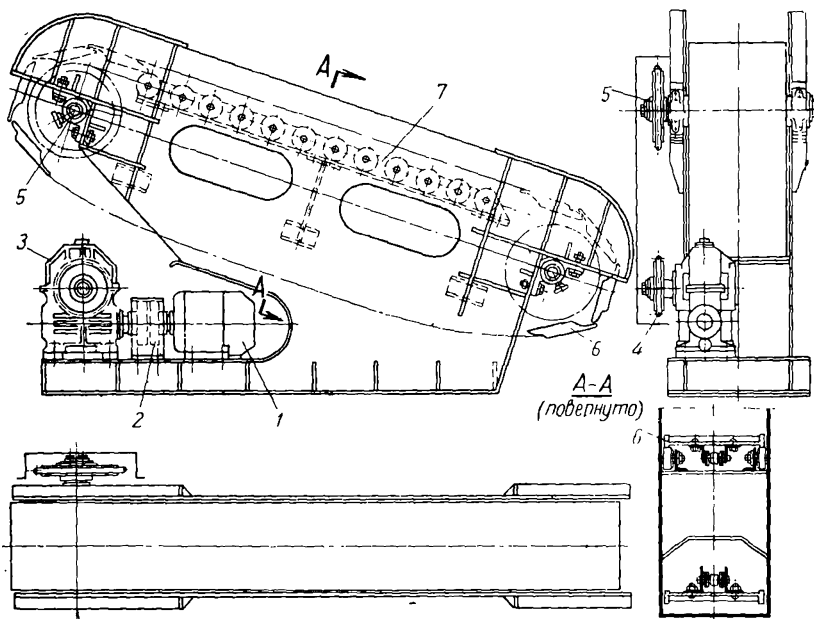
Наклонный пластинчатый транспортер: 1 — электродвигатель; 2 — упругая муфта; 3 — редуктор; 4 — звездочка; 5 — узел приводного вала; 6 — ходовая часть; 7 — металлоконструкция транспортера
